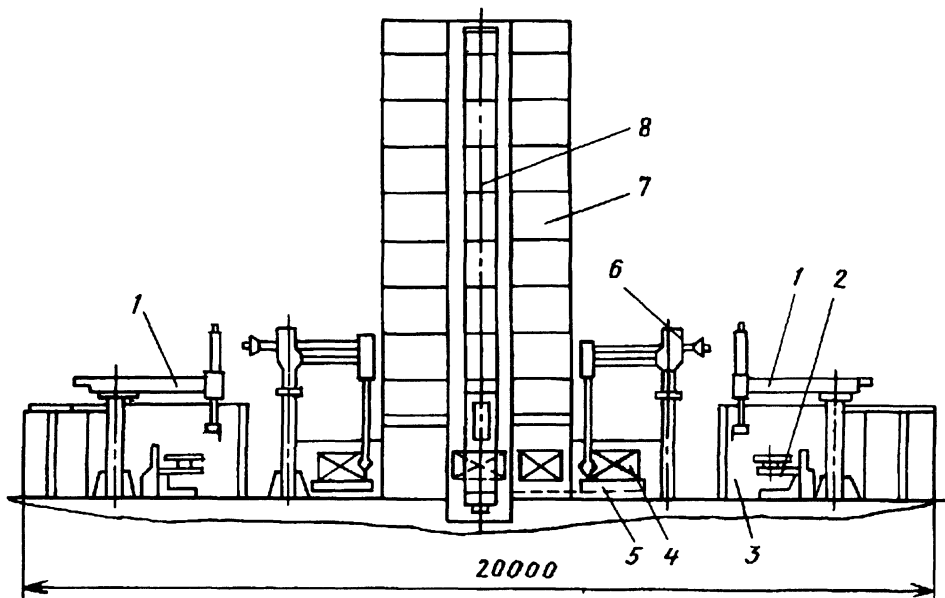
Схема типовой роботизированного участка для дуговой сварки с несколькими рабочими местами
